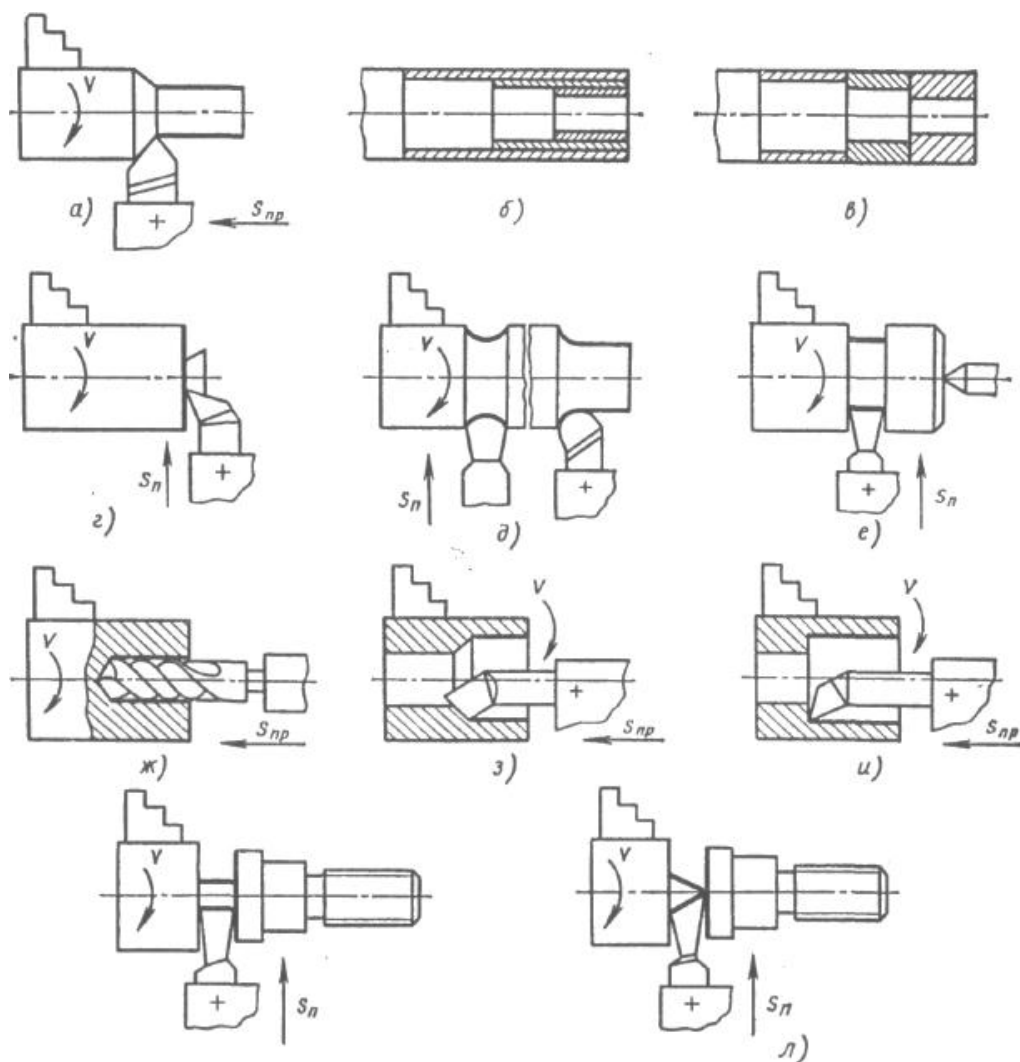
Схемы обработки заготовок на токарных станках: а – точение наружной цилиндрической поверхности (методы обработки: б – многопроходная; в – однопроходная), г – подрезание торцевой поверхности; д – обработка фасонных поверхностей; е – обработка канавок; ж – сверление отверстия; з, и – растачивание; л – варианты отрезки детали
